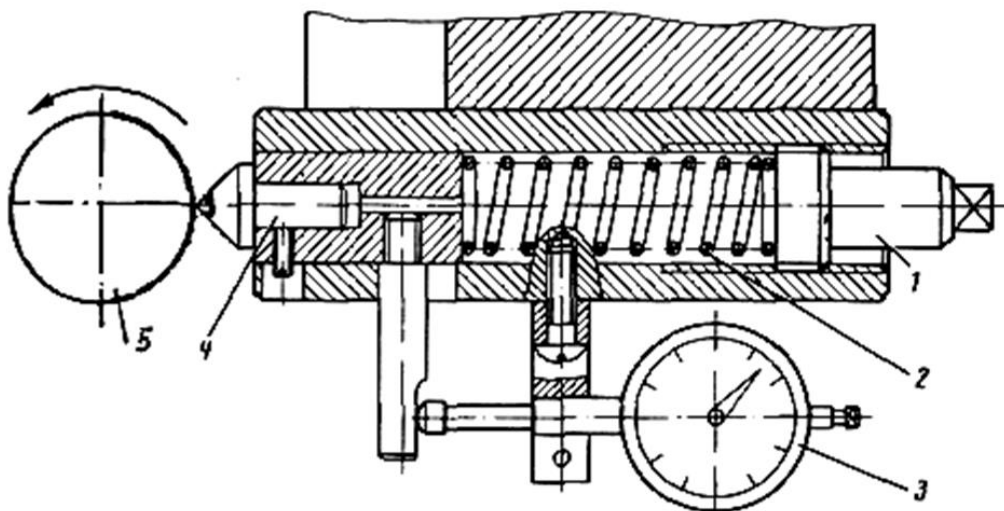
Схема процесса алмазного выглаживания: 1 – регулировочный винт; 2 – пружина; 3 – индикаторная головка; 4 – наконечник с алмазом; 5 – заготовка
